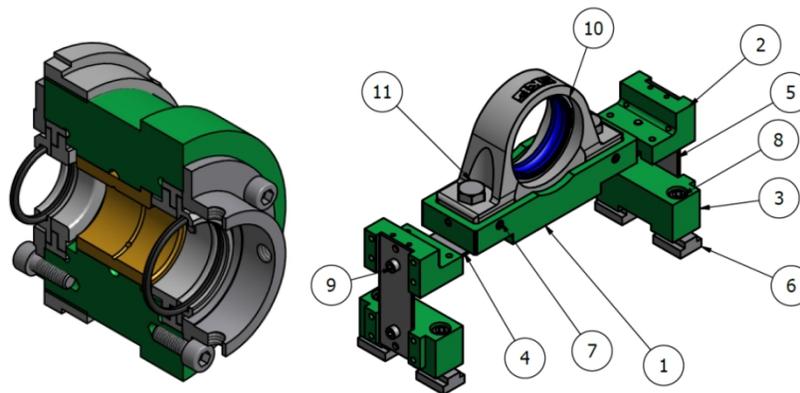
Izquierda: Cuerpo del cojinete; Derecha: Pedestal
